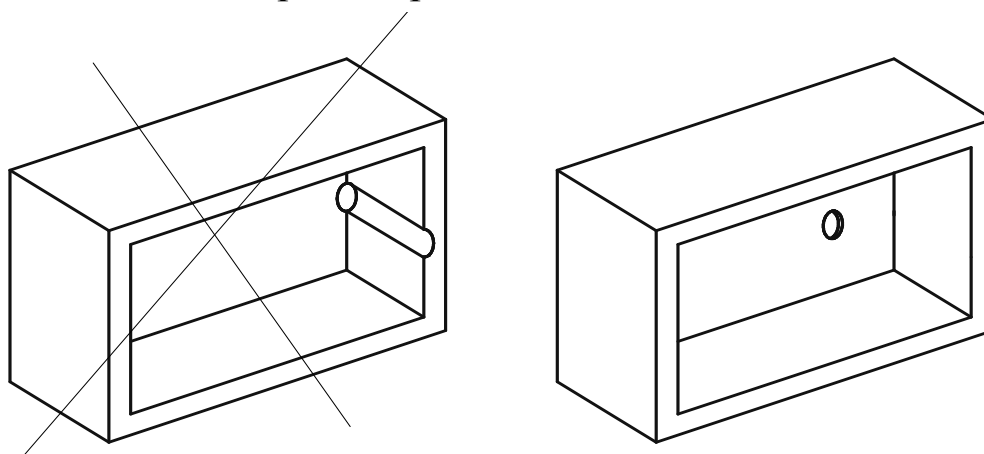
Схема технологичной детали по удобству обработки отверстий
